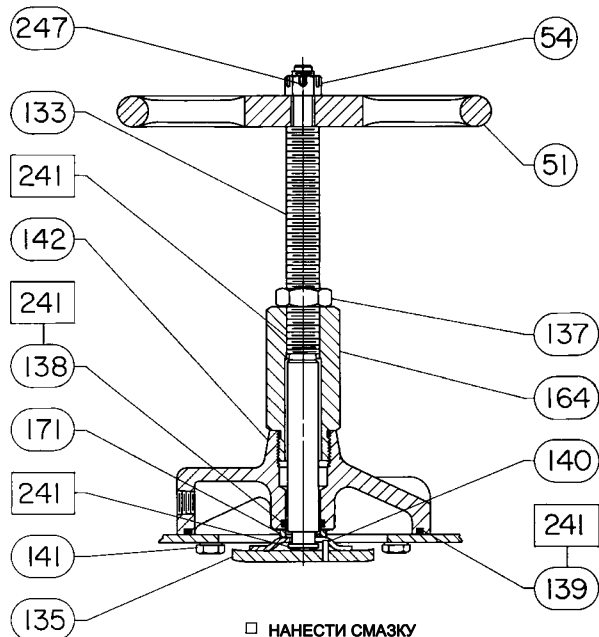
Монтаж типа Н для оборудования с клиновыми валами 44,5 или 50,8 мм (1-3/4 или 2 дюйма)
